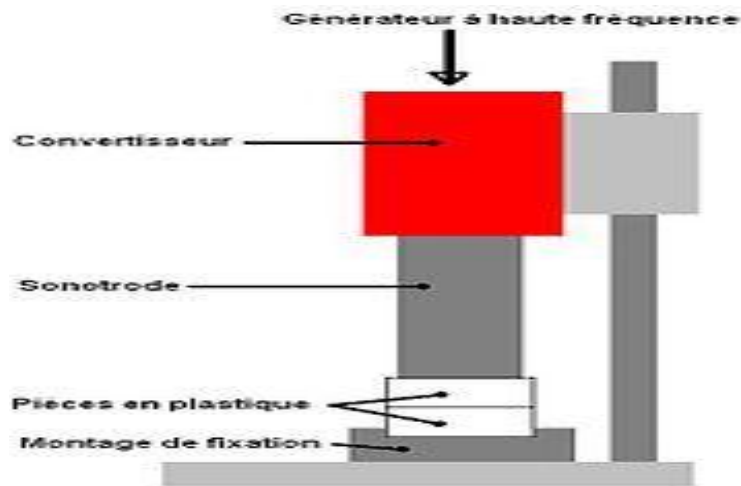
Principe de soudage haut fréquence.
